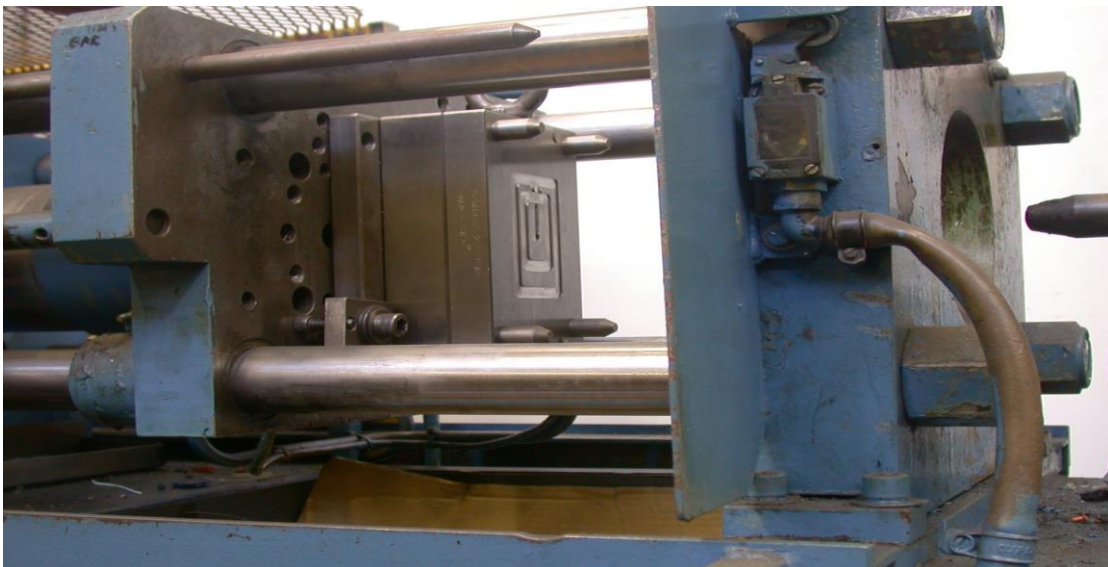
Molde para fabricar un clip de plástico para papel.
